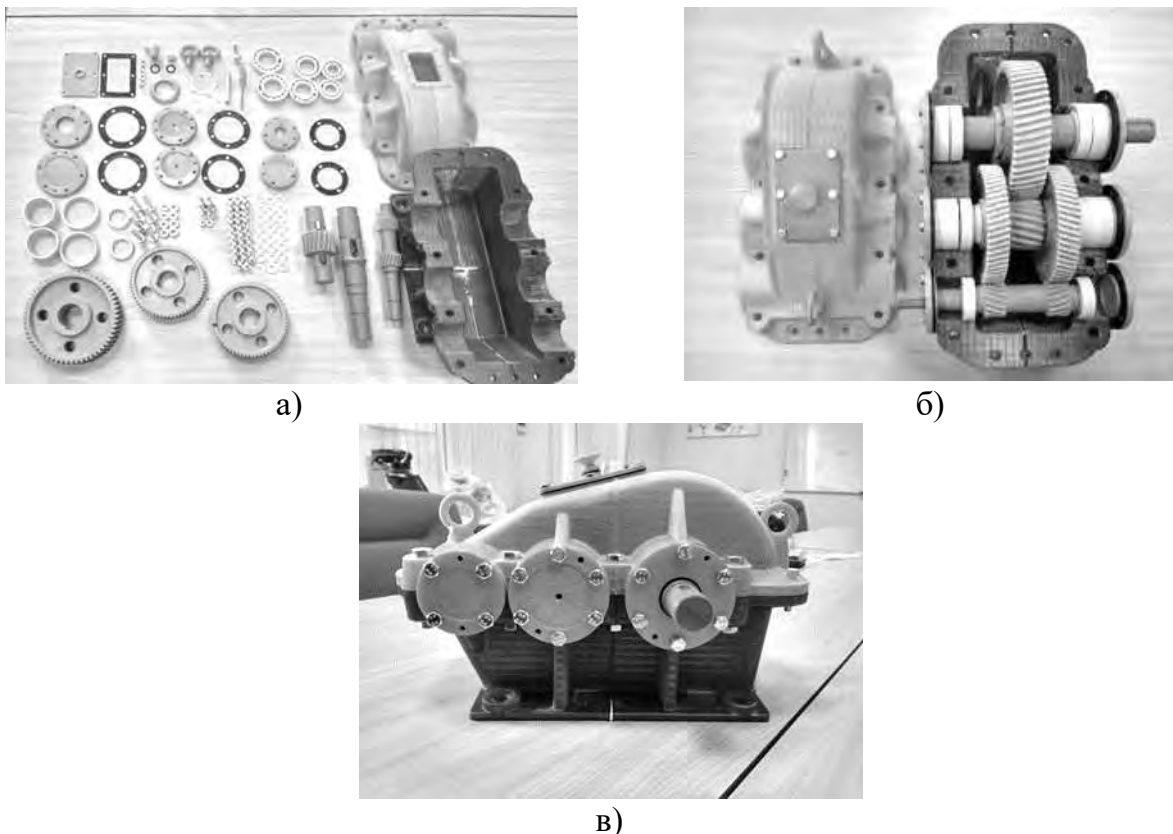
Цилиндрический редуктор: а) детали редуктора, полученные 3D печатью; б) редуктор со снятой крышкой; в) редуктор в сборе.
